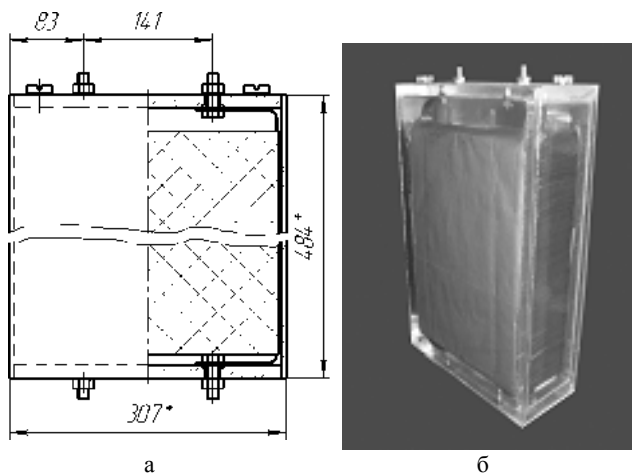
Конденсатор КИМ-136: а – габаритные размеры, б – внешний вид
